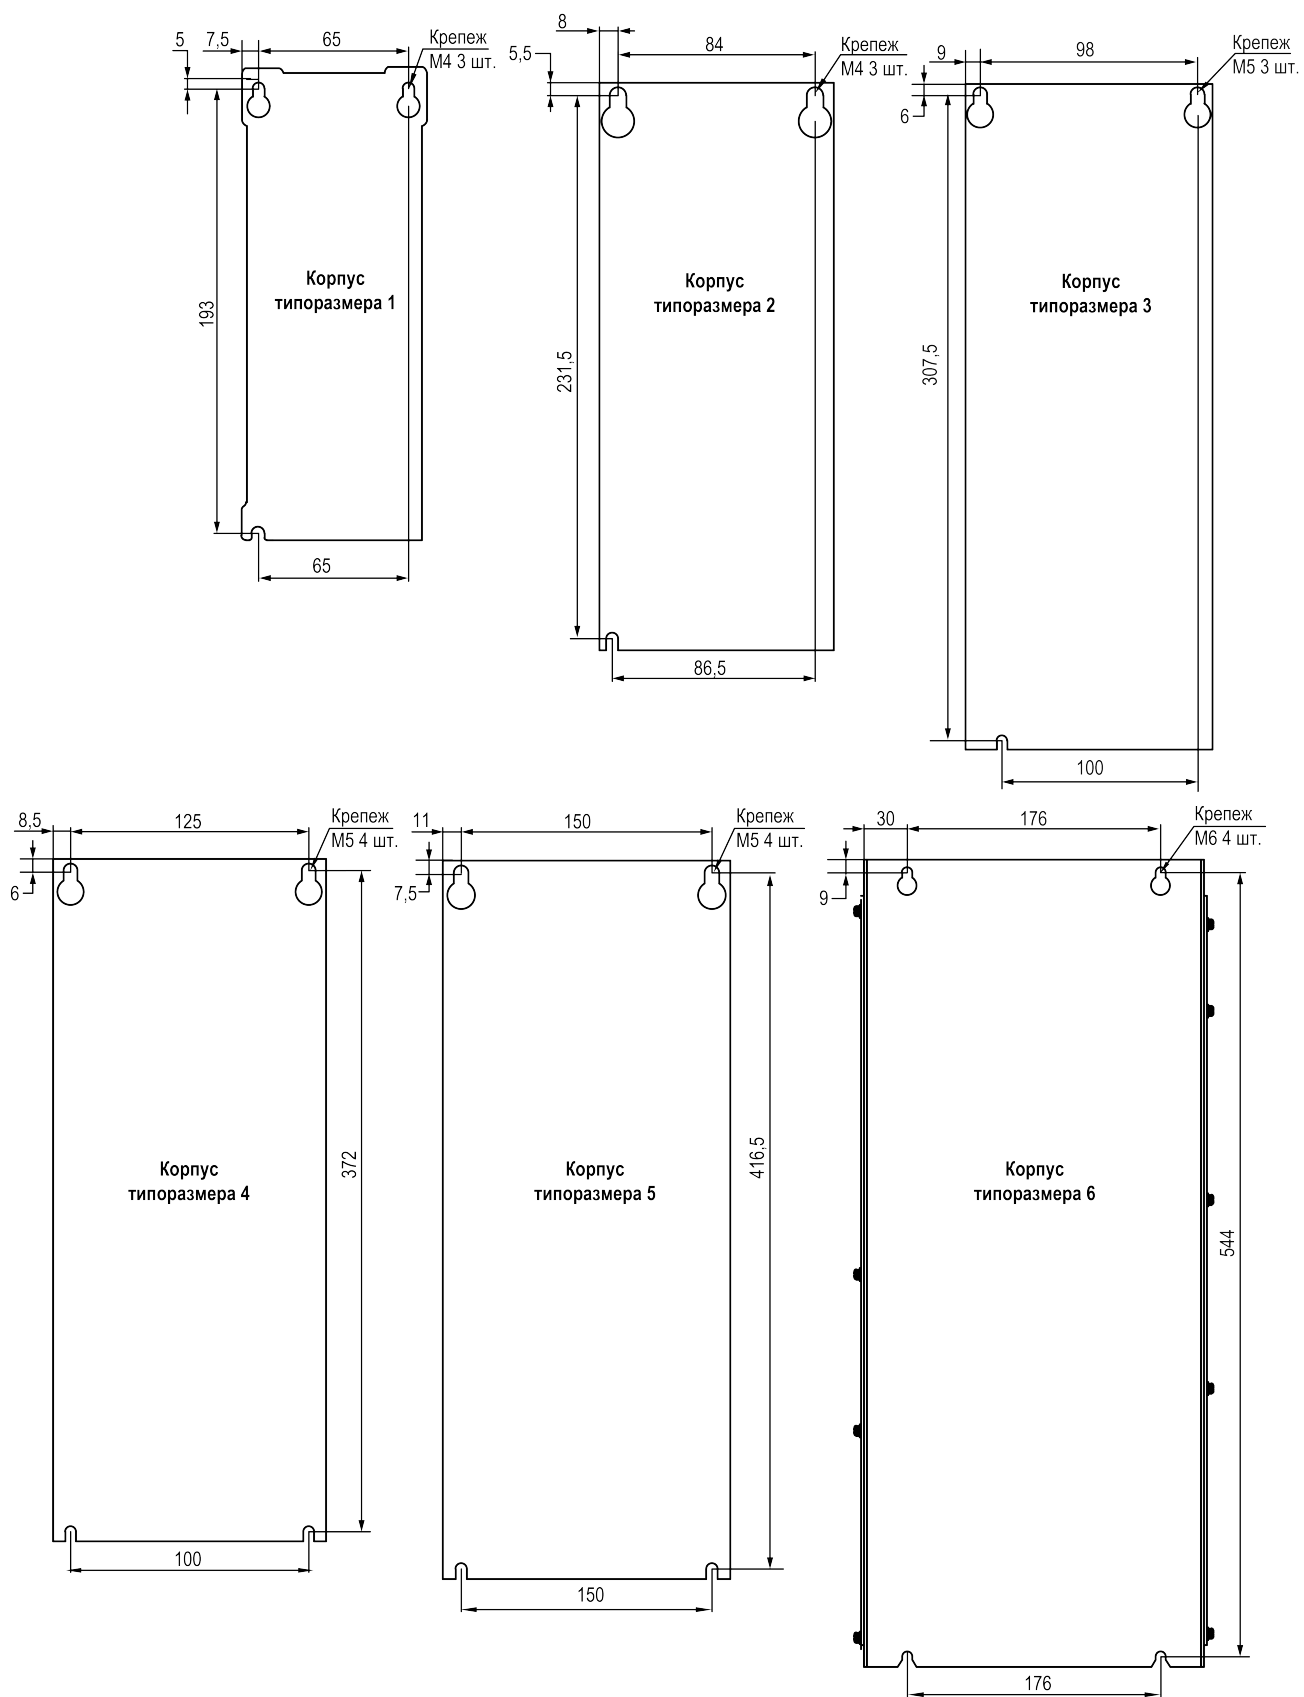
Присоединительные размеры для корпусов типоразмеров 1–6
